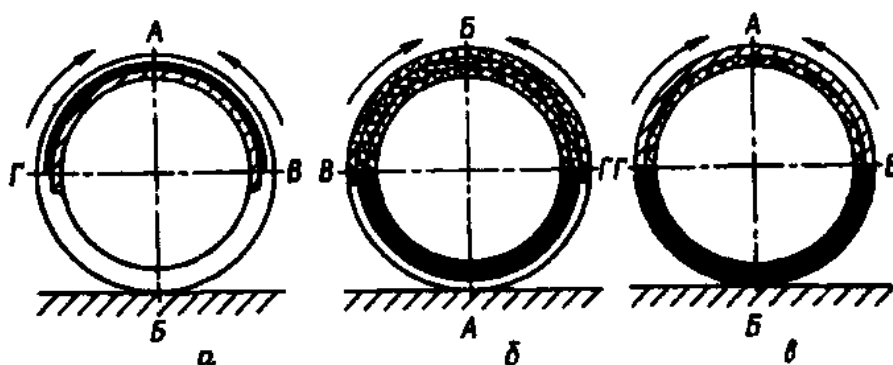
Порядок сварки стыка труб с поворотом на 180°
